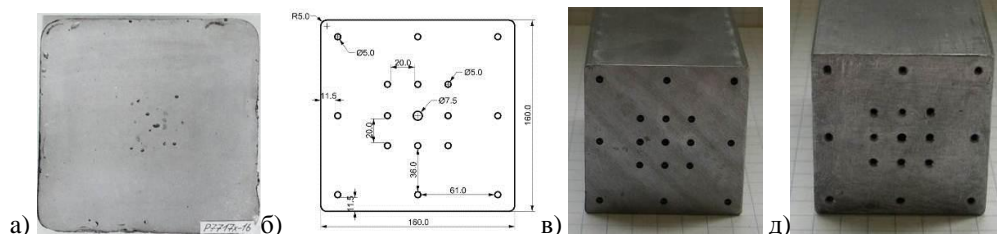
Вид образца с нанесенными дефектами, сравненные с реальными дефектами непрерывнолитой заготовки. Внутренние и подповерхностные поры отливки:
